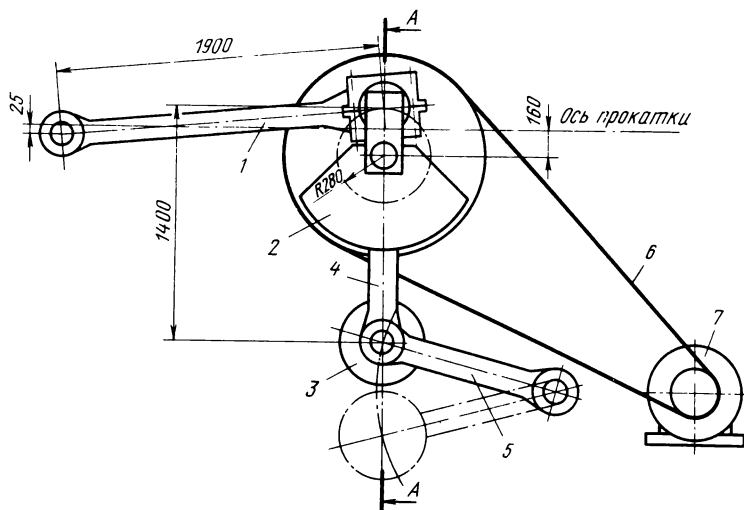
Приводной механизм стана КПВ 25 ВМР
